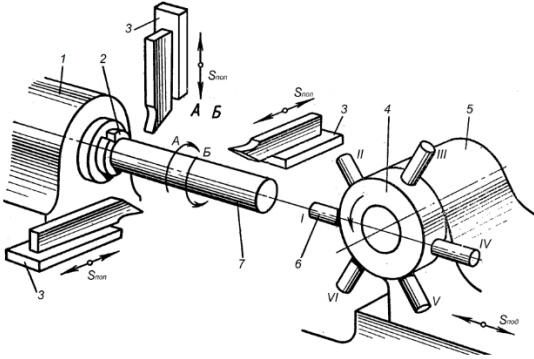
Схема роботи токарно-револьверного автомата
